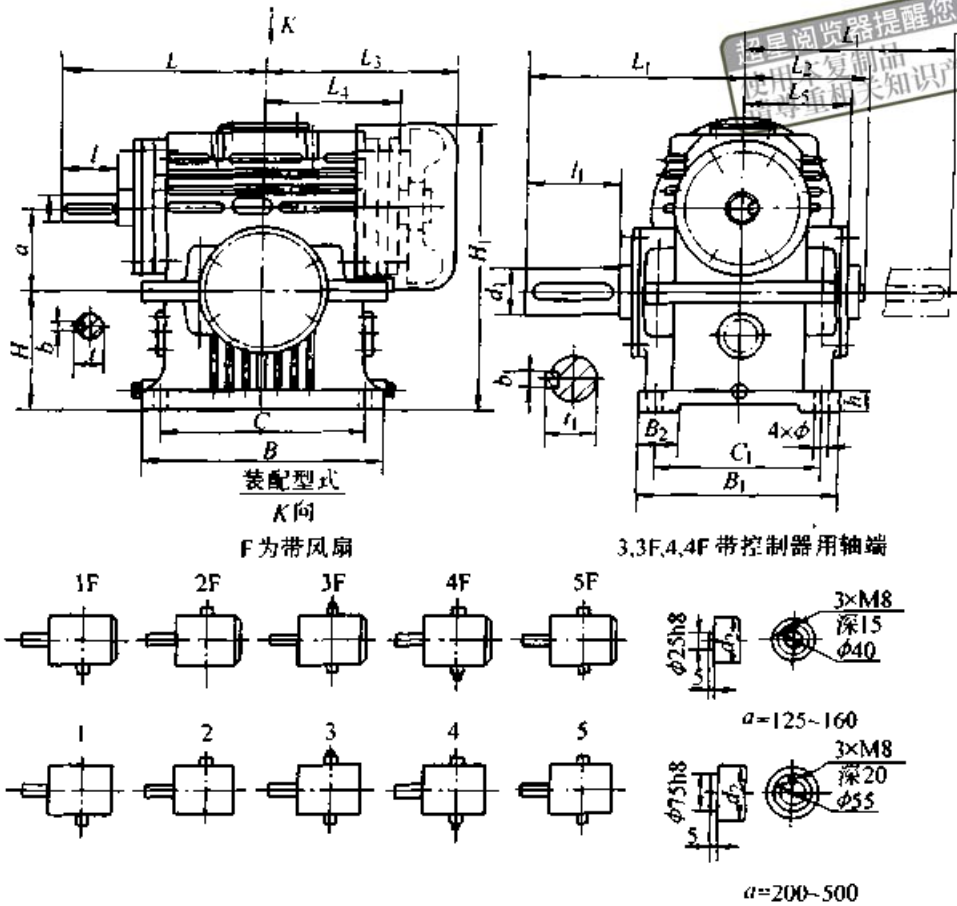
TPA 型减速器外形尺寸及装配型式
